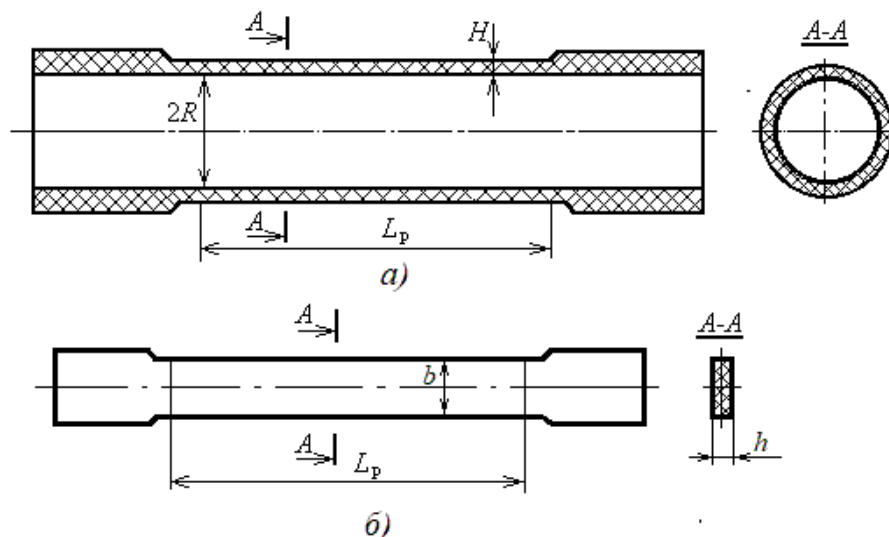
Эскизы образцов из КМ, часто применяемых при проведении опытов: а) тонкостенный цилиндрический образец; б) образец-лопатка
